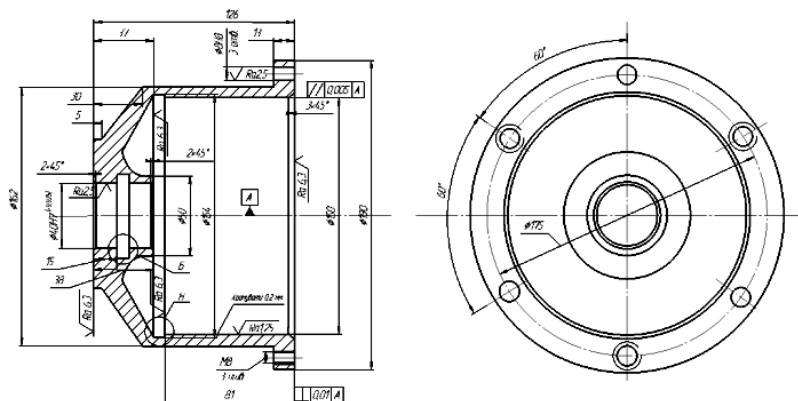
Креслення деталі корпуса одностороннього гідроциліндра
